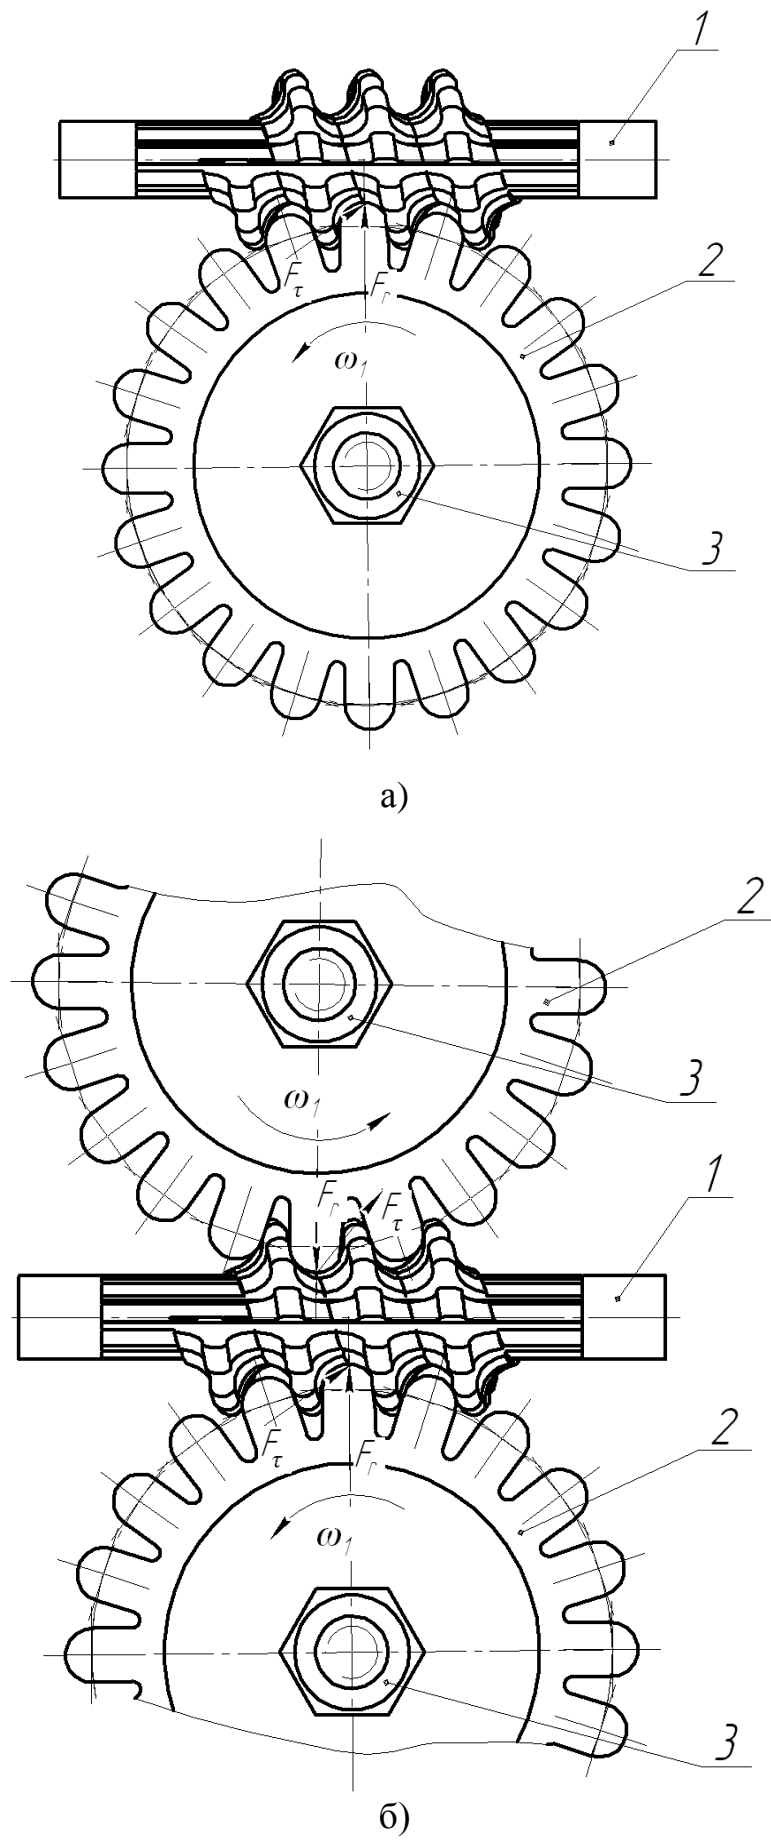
Механiчне оброблення профiльною черв'ячною фрезою однієї заготовки а) та одночасно двох заготовок
